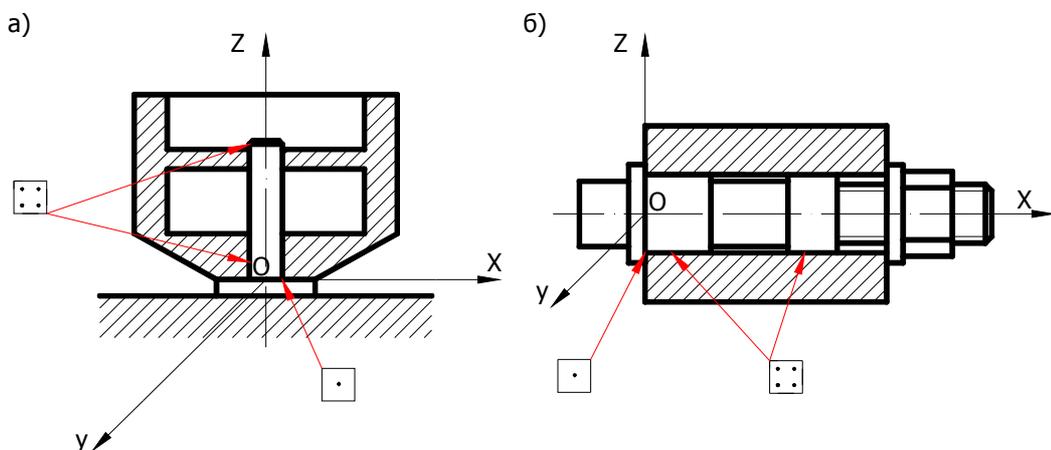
Схемы установки детали на высокий цилиндрический палец (а) и цилиндрическую оправку (б).
